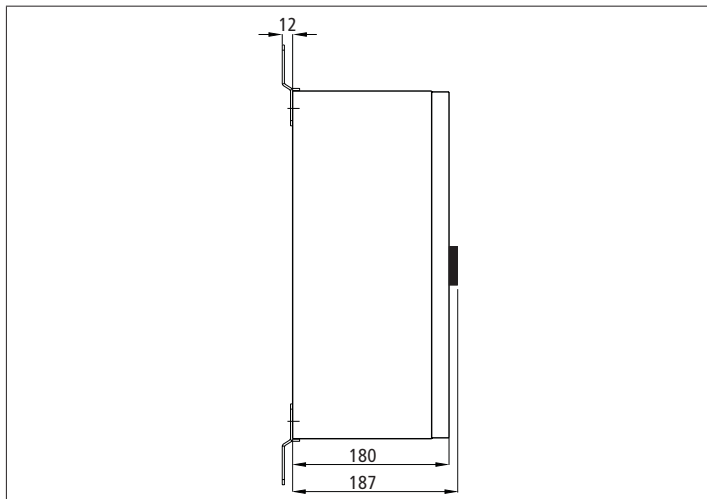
Seitenansicht SVG 522/TSK 03 mit Befestigungslaschen
